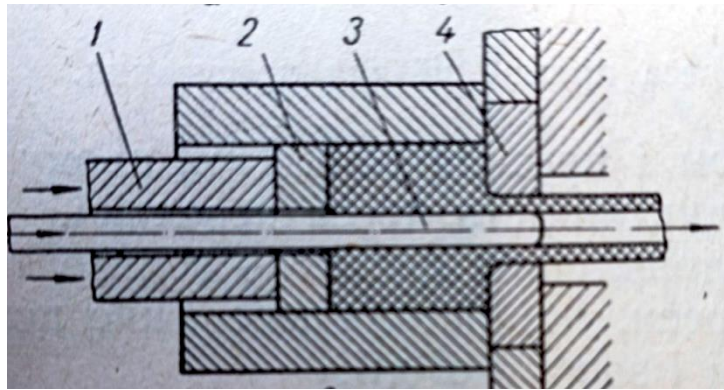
Схема процесу прямого пресування трубчастих виробів: 1 - пуансон; 2 – прес-шайба; 3 – сталева голка; 4 – зовнішня поверхня матриці
